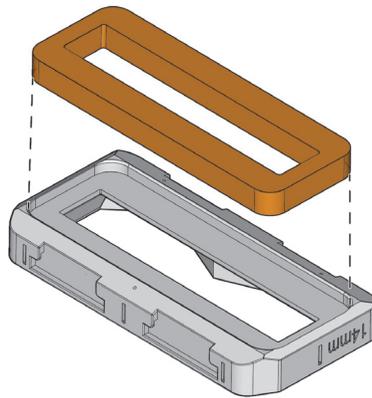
Nouveau joint en mousse et plaque de ligne à retard
